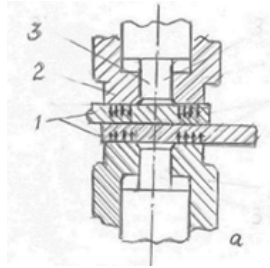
Схема холодного точкового зварювання з попереднім обтисненням
